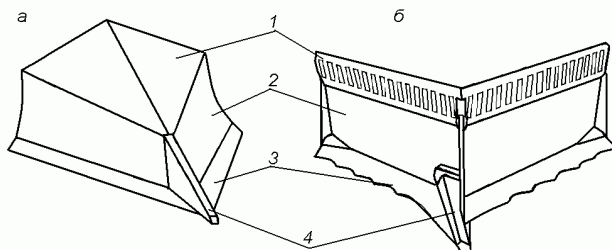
Клиновидный (а) и двухкорпусный (б) кусторезные отвалы: 1 – защитная конструкция; 2 – отвальная поверхность; 3 –режущая кромка; 4 – колун.
